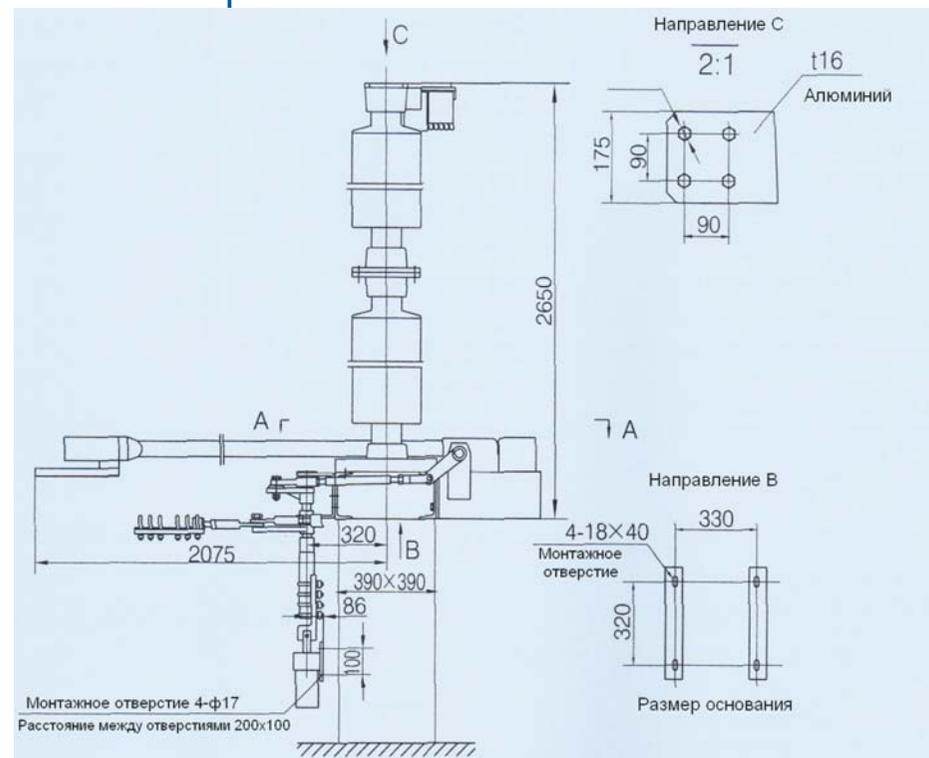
Внешний вид и размеры заземлителя JW□-252
